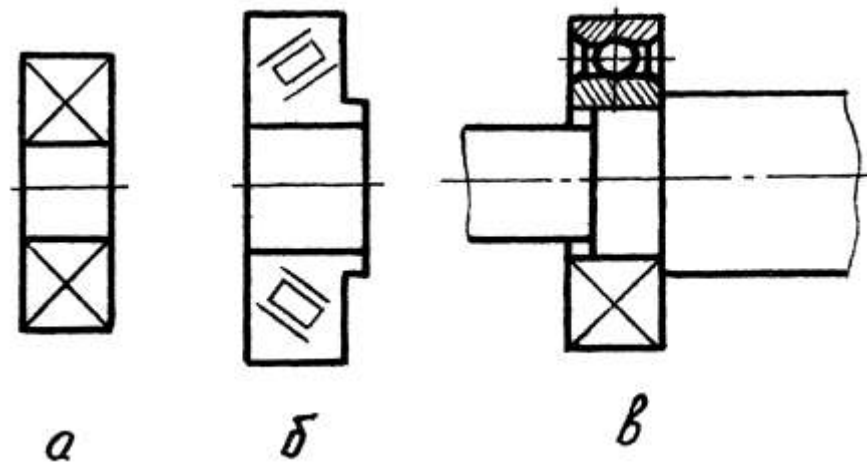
Варианты изображения подшипников на сборочном чертеже
